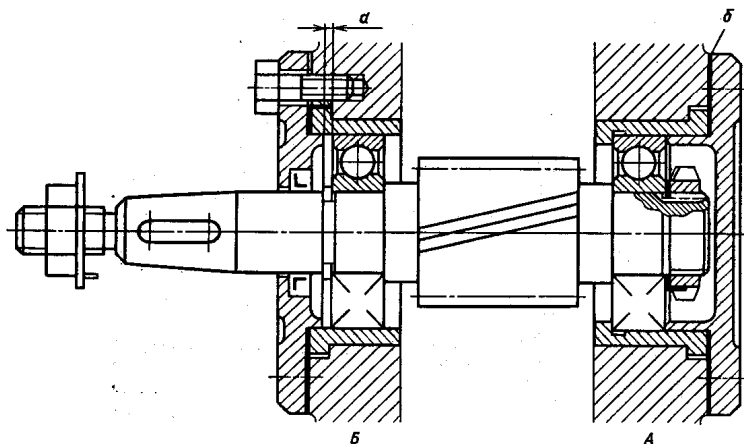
Вал установлен на радиальных подшипниках; правый – фиксированный, левый – «плавающий»
